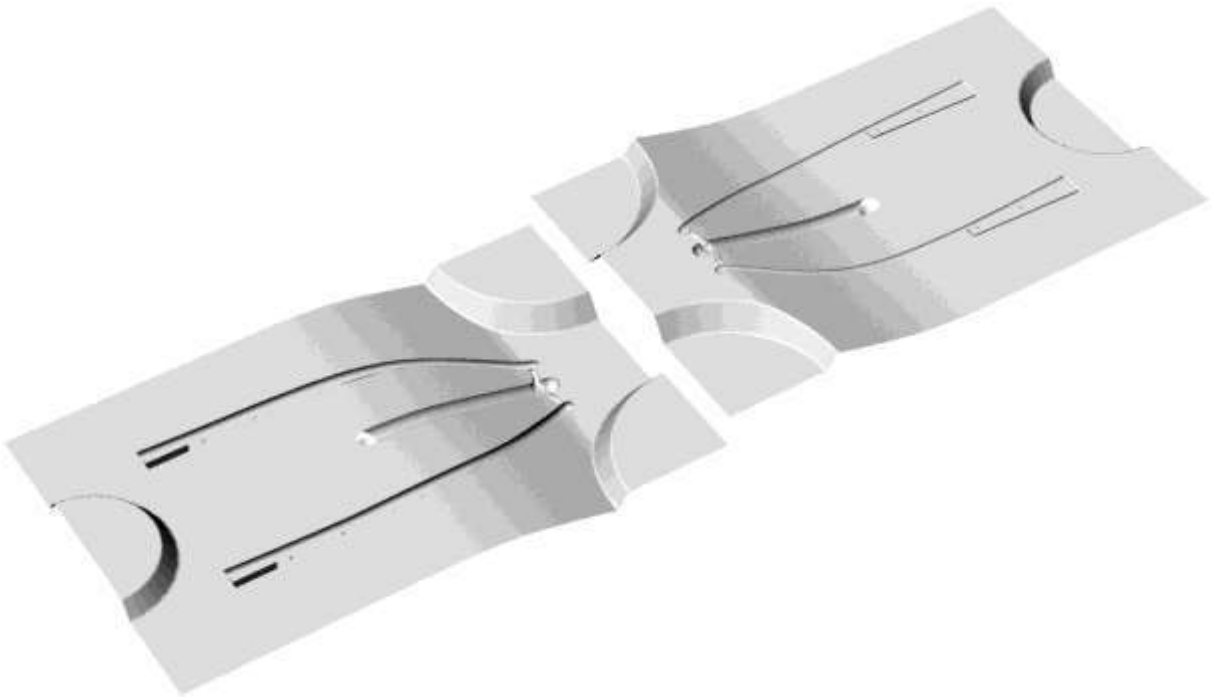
Molde de injeção modelado em computador / Fonte: Elaboração Própria
